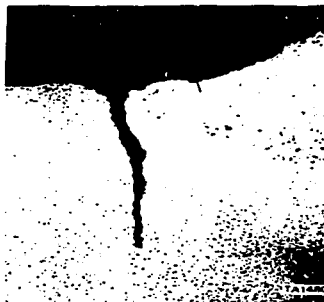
Corrosión por fatiga originada a partir del pie de la soldadura en acero al carbono [32].
